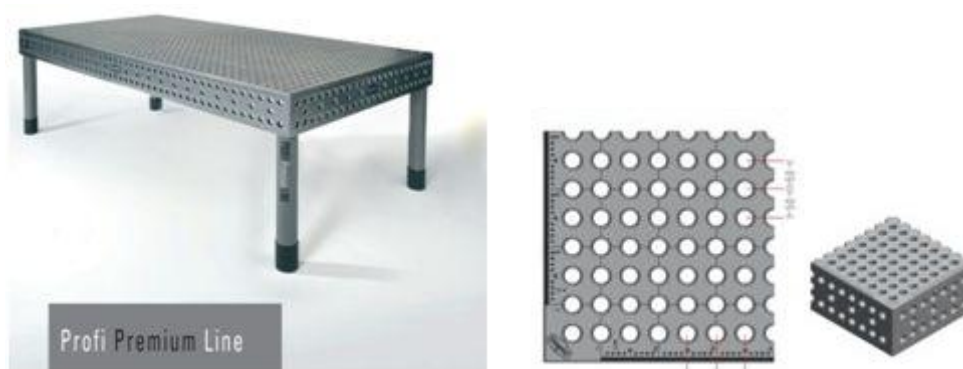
Сварочный универсальный 3D стол системы Demmeler
